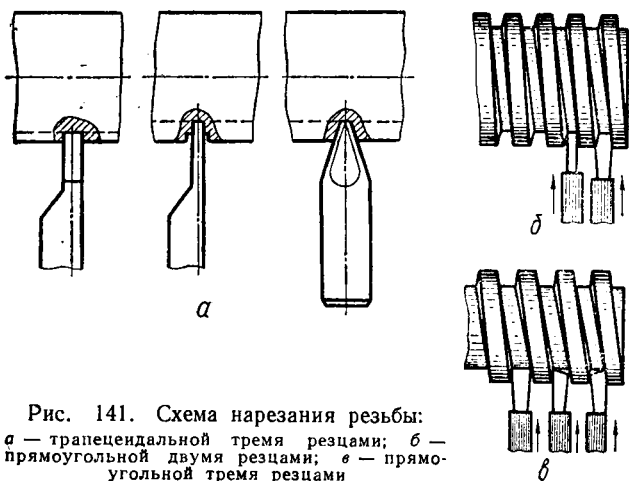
Схема нарезания резьбы: а — трапецидальной тремя резцами; б — прямоугольной двумя резцами; в — прямоугольной тремя резцами
